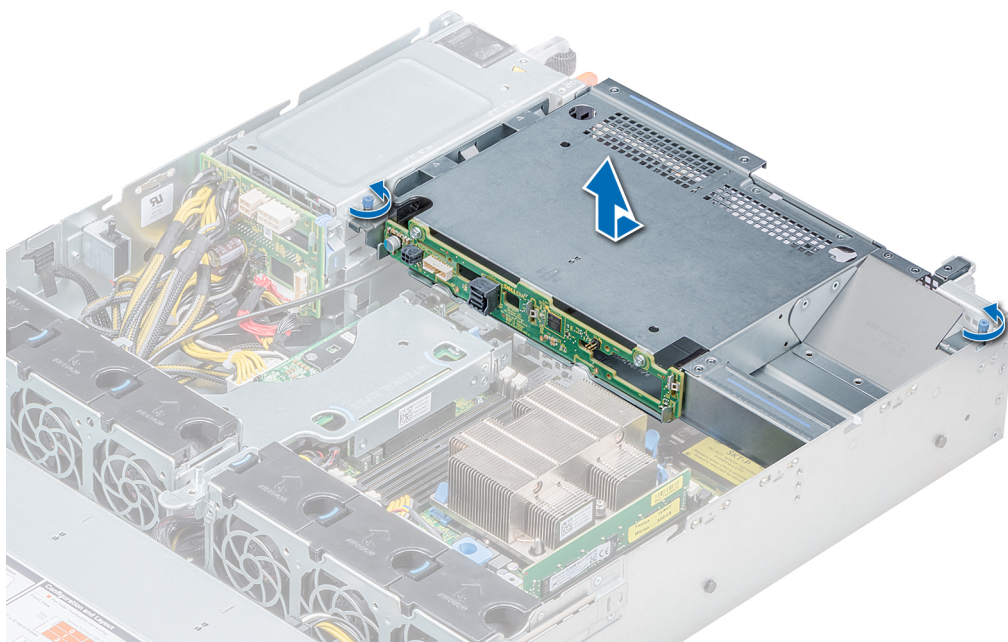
Entfernen des hinteren Laufwerksgehäuses
